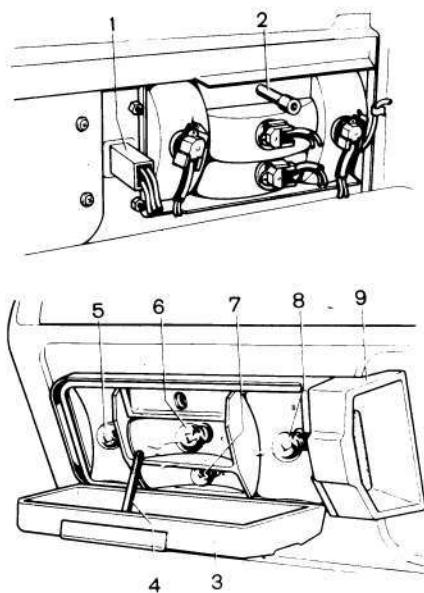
Задний фонари и фонары освещения номерного знака: 1 — колодка; 2 — гайка; 3 — рассеиватель; 4 — шпилька; 5 — лампа указателя поворота; 6 — лампа света заднего хода; 7 — лампа габаритного света; 8 — лампа стоп-сигнала; 9 — фонарь освещения номерного знака
